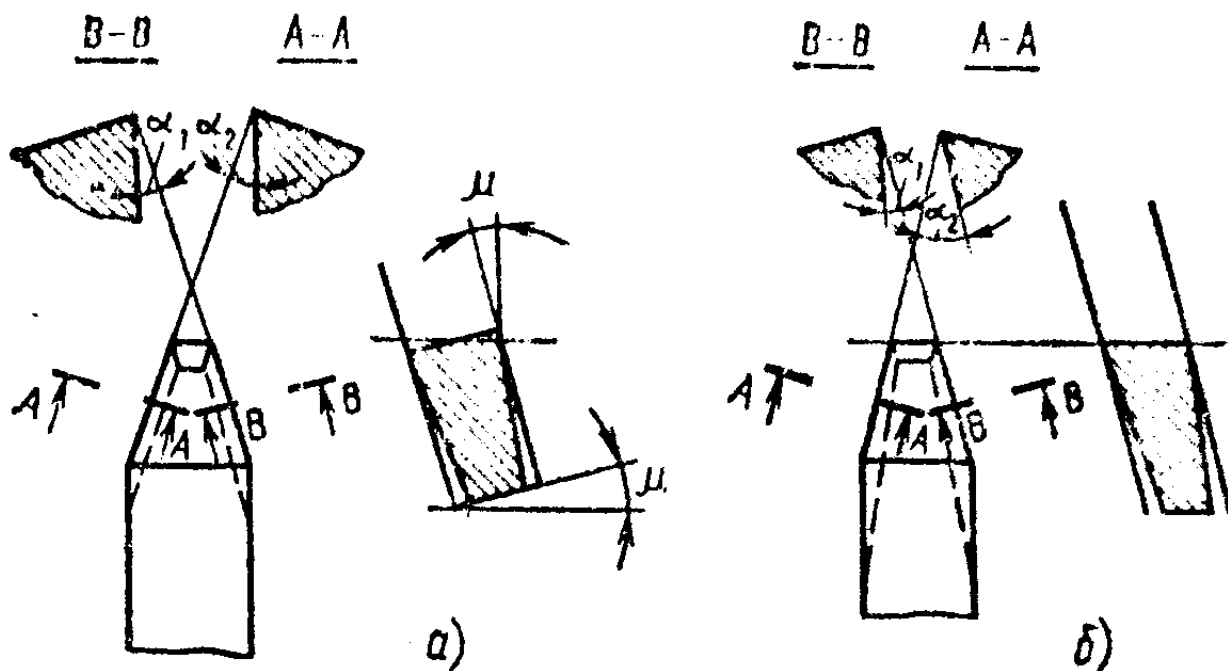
Установка резьбового резца при нарезании трапецеидальной резьбы:
